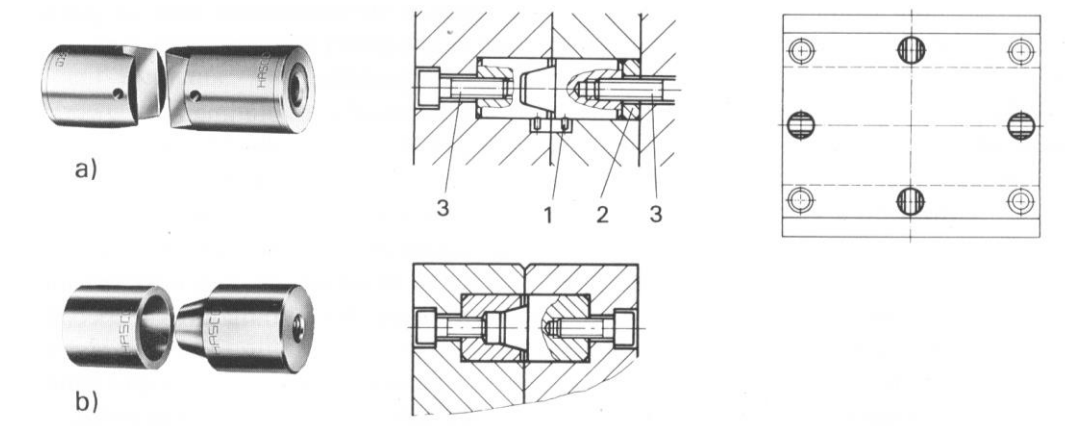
Elemento de centrado tipo plano (a) y tipo cónico (b)
